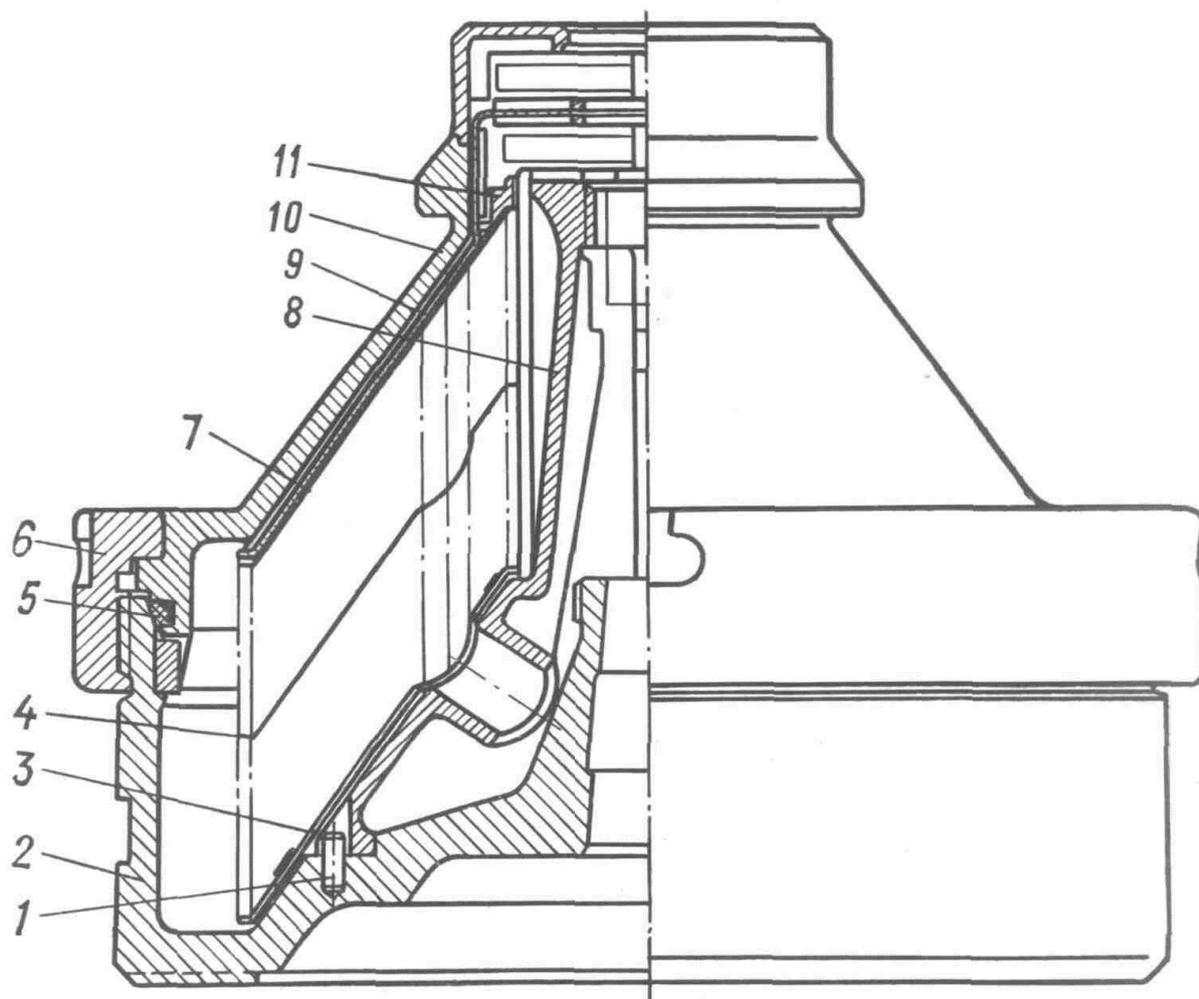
Барабан сепаратора Г9-ОСП: 1 – штифт; 2 – основание барабана; 3 – нижняя тарелка; 4 – тарелки; 5 – уплотнительное кольцо; 6 – большое затяжное кольцо; 7 – верхняя тарелка; 8 – тарелкодержатель; 9 – разделительная тарелка; 10 – крышка барабана; 11 – диск верхней тарелки
